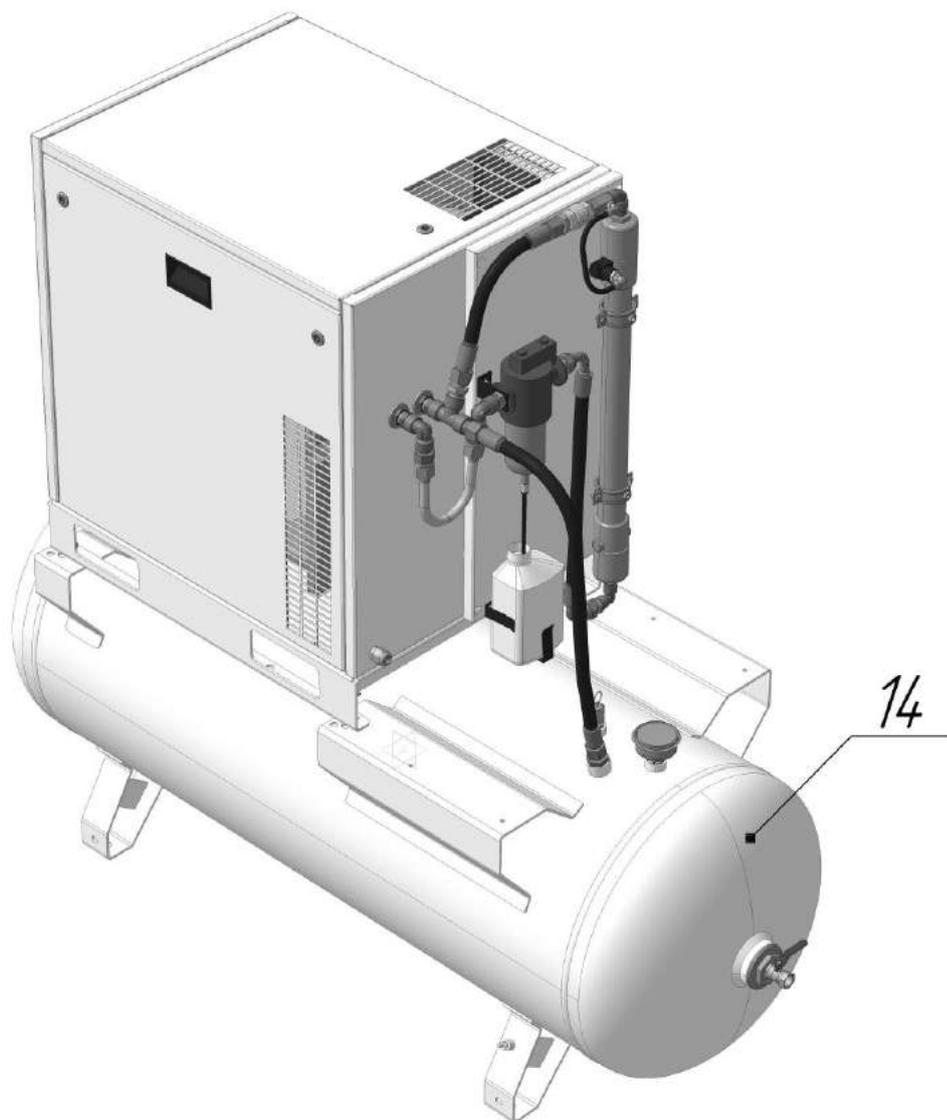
Общий вид компрессорных установок КС3-...-270М(-1М), КС5-...-270М(-1М)
